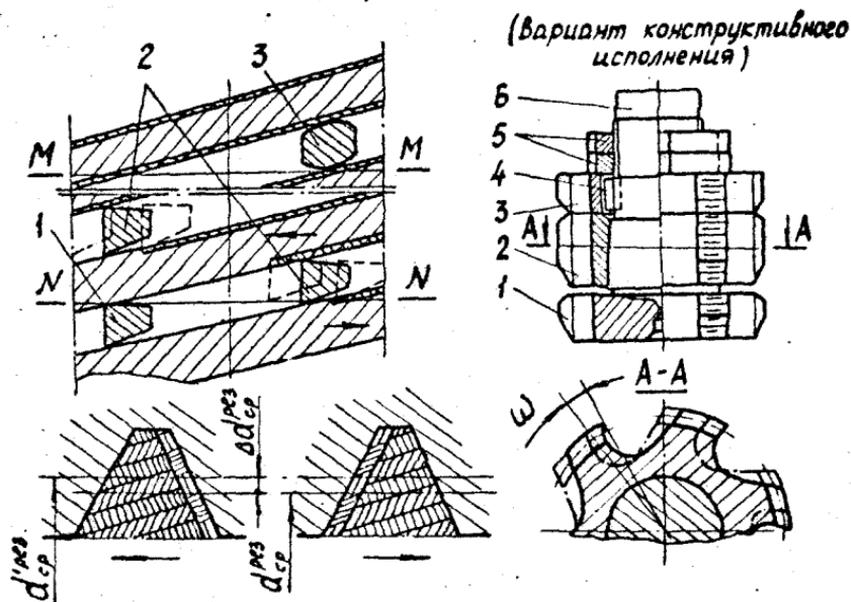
Конструкция регулируемого метчика для нарезания сквозных резьбовых отверстий и схема формирования профиля резьбы
